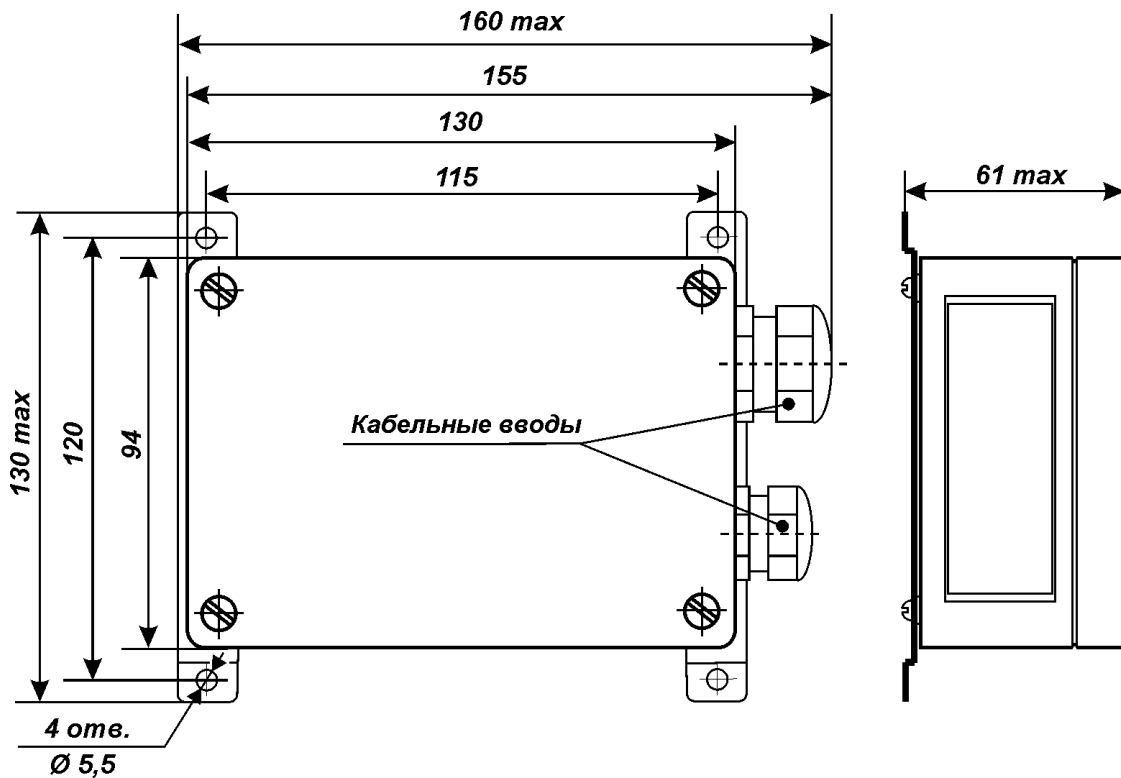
Зовнішній вигляд та габаритні розміри ПК-10-1
